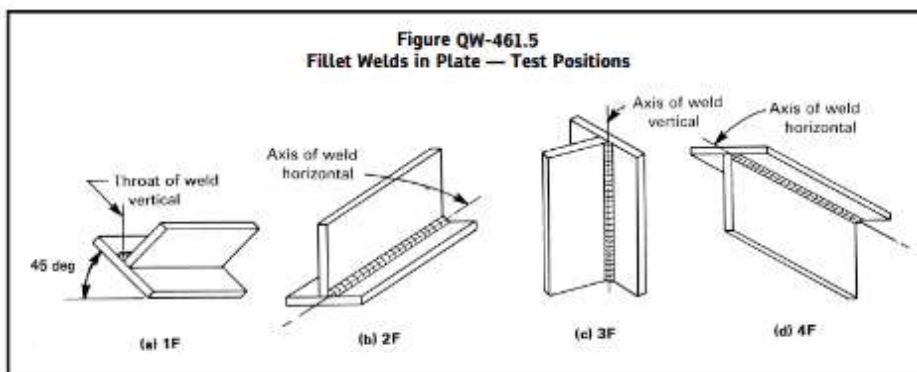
Posiciones de soldadura de filete entre láminas.
